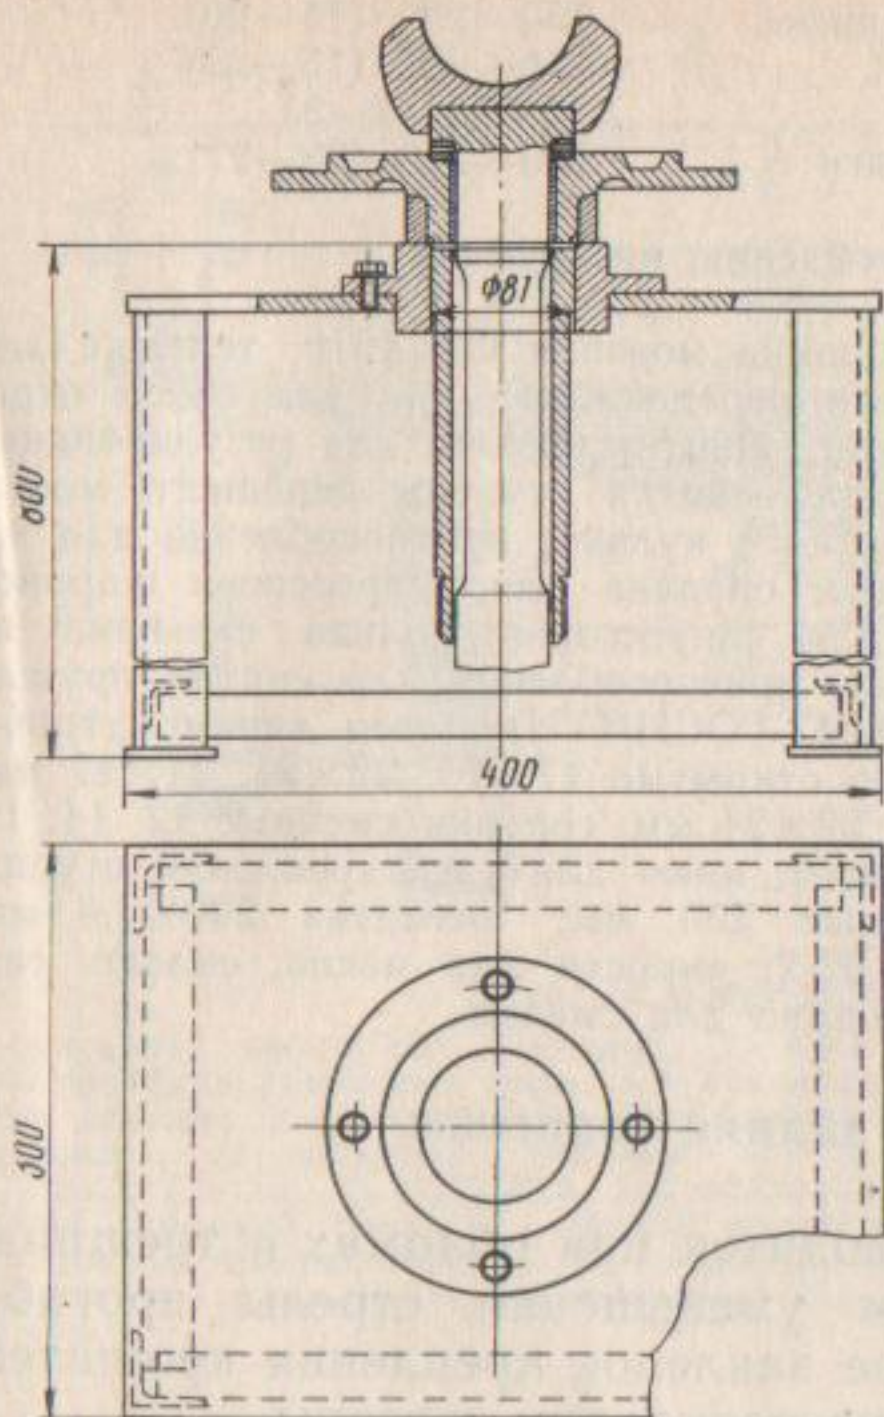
Общий вид приспособления для сборки цапфы поворотного кулака
